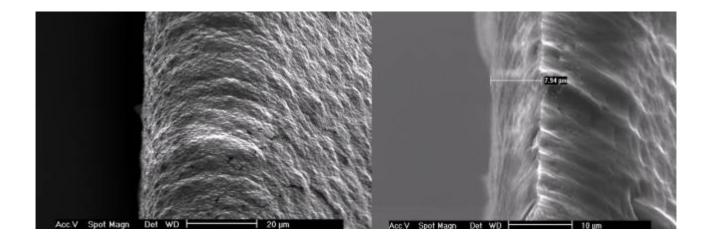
Aufsicht auf eine diamantbeschichtete Schneidkante vor (links) und nach dem Schärfen (rechts).
